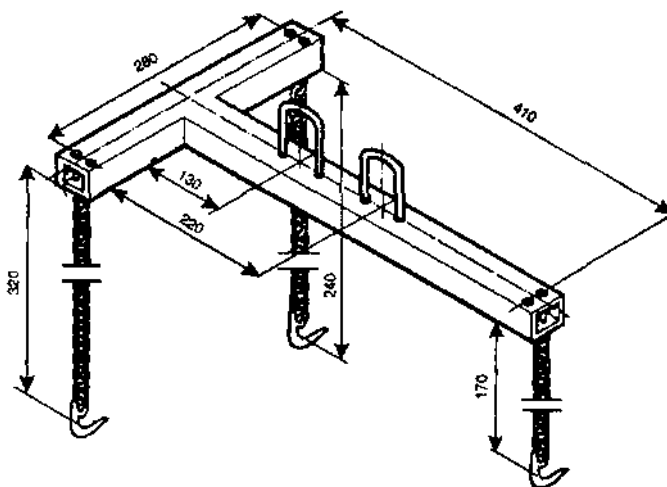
Приспособление для подвески силового агрегата.
